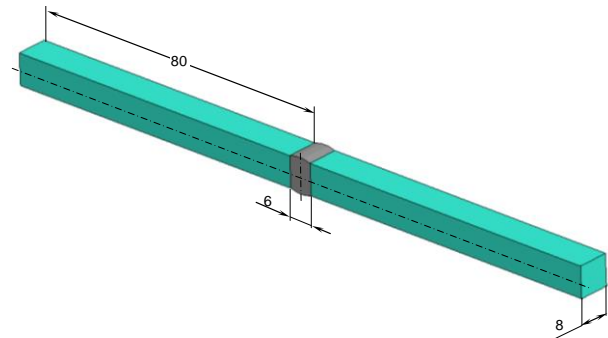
Конструктивна схема зразка зварного з'єднання для випробувань
